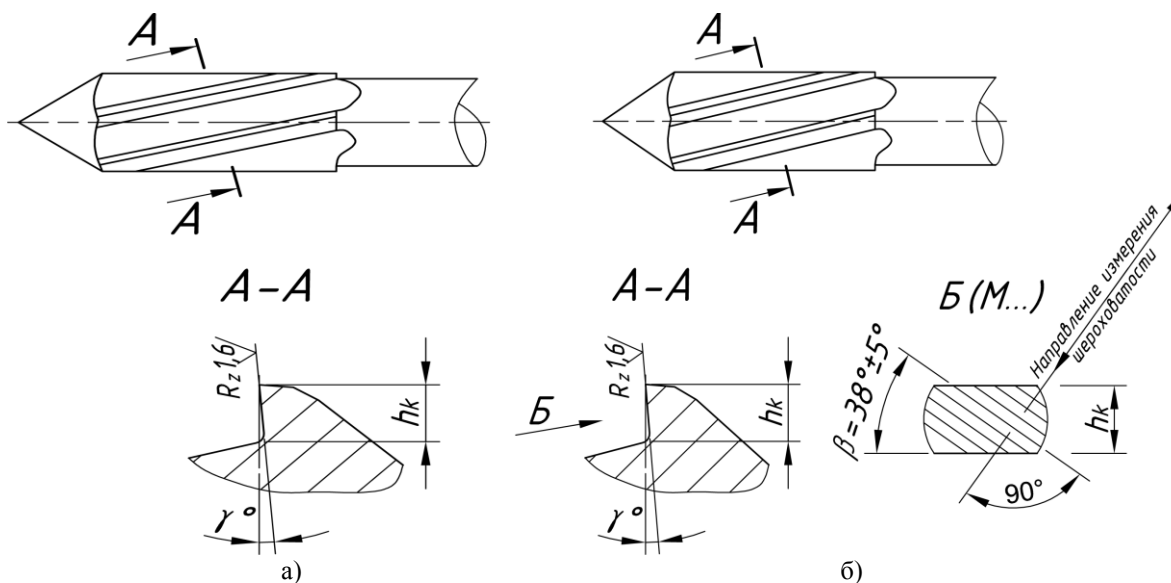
Оформление требований к шероховатости винтовой передней поверхности на рабочих чертежах инструментов
